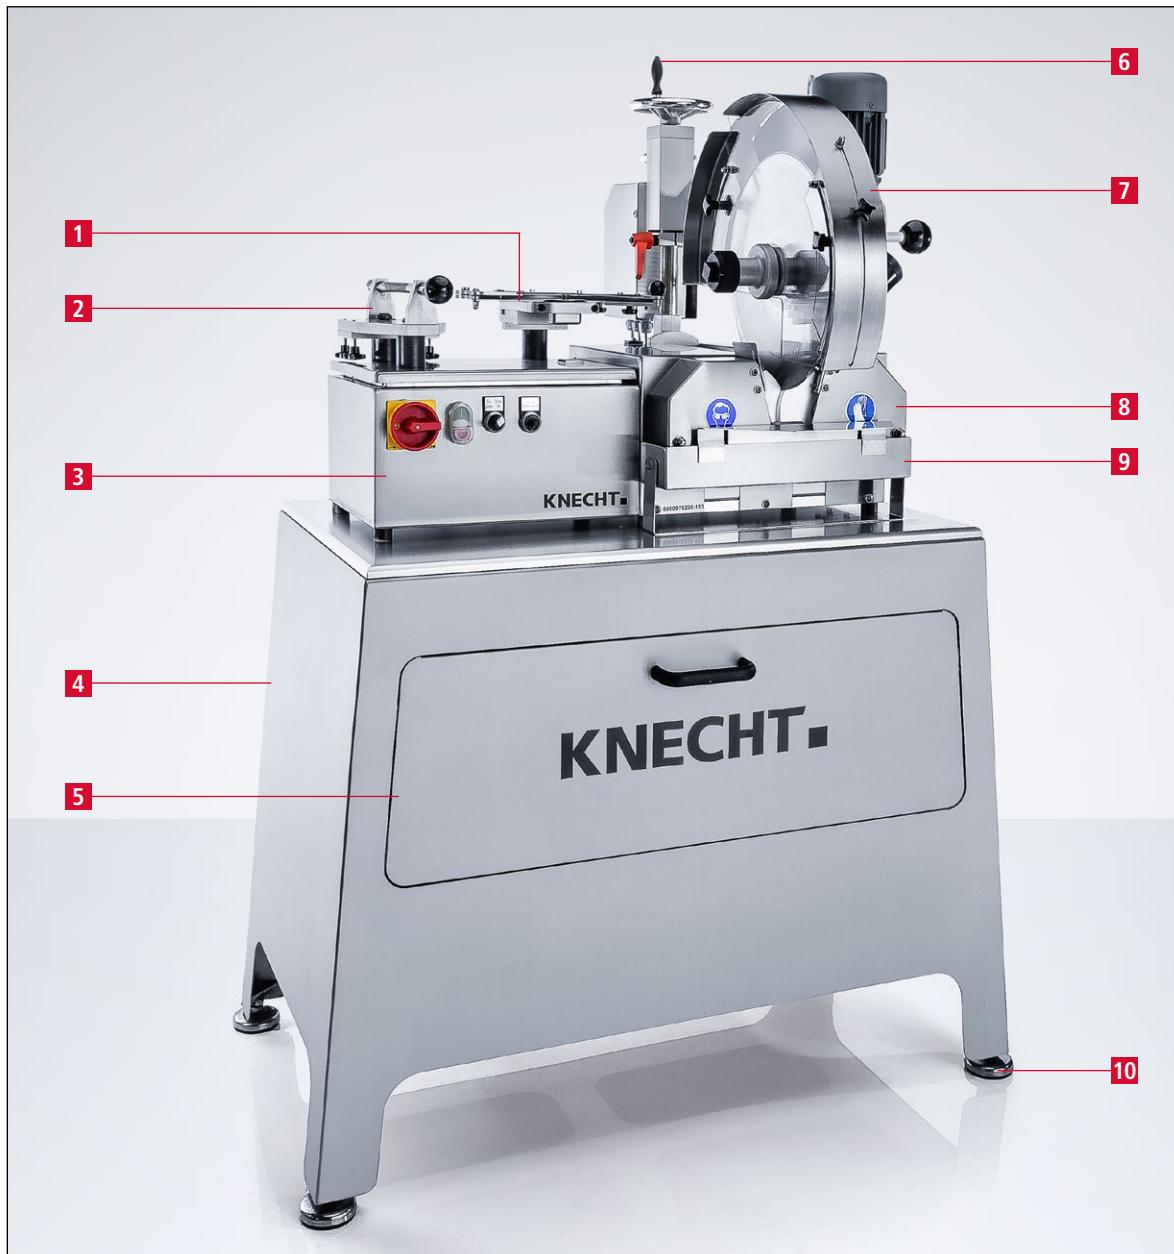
Общий вид станка для заточки дисковых ножей
